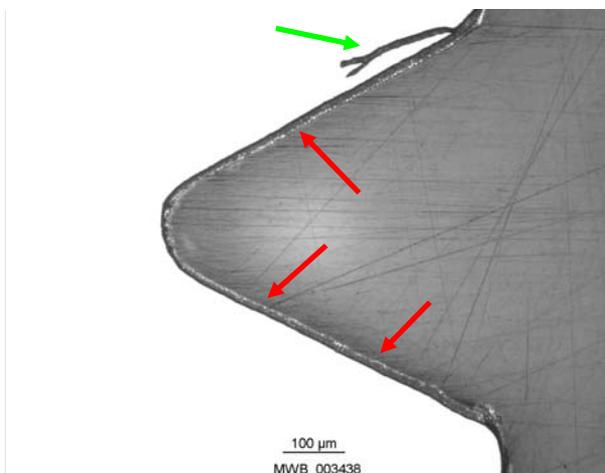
Unbeschädigte Beschichtung (rote Pfeile) und Anrisse (grüner Pfeil) auf den Gewindeflanken.
